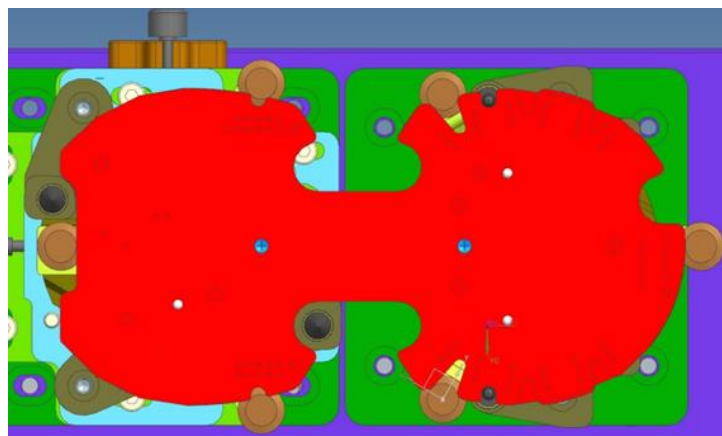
3D CAD-модель вигляду знизу затиснутої друкованої плати
